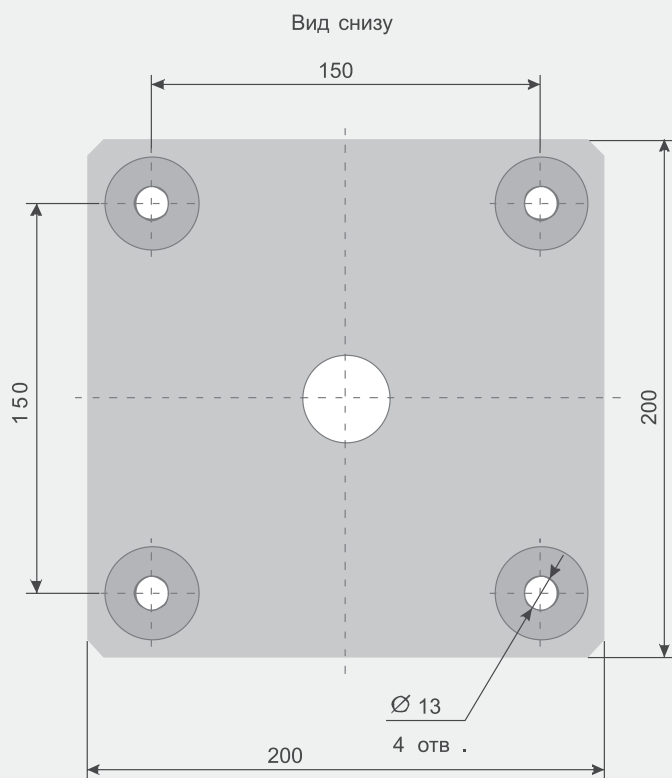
Присоединительные размеры изолирующего основания ОПН-РК.
